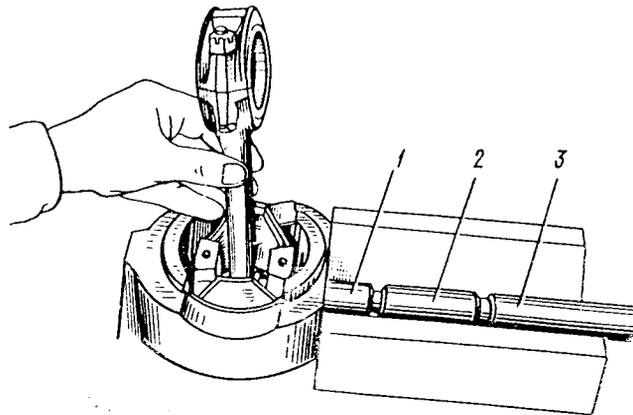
Einpressvorrichtung für Kolbenbolzen:
